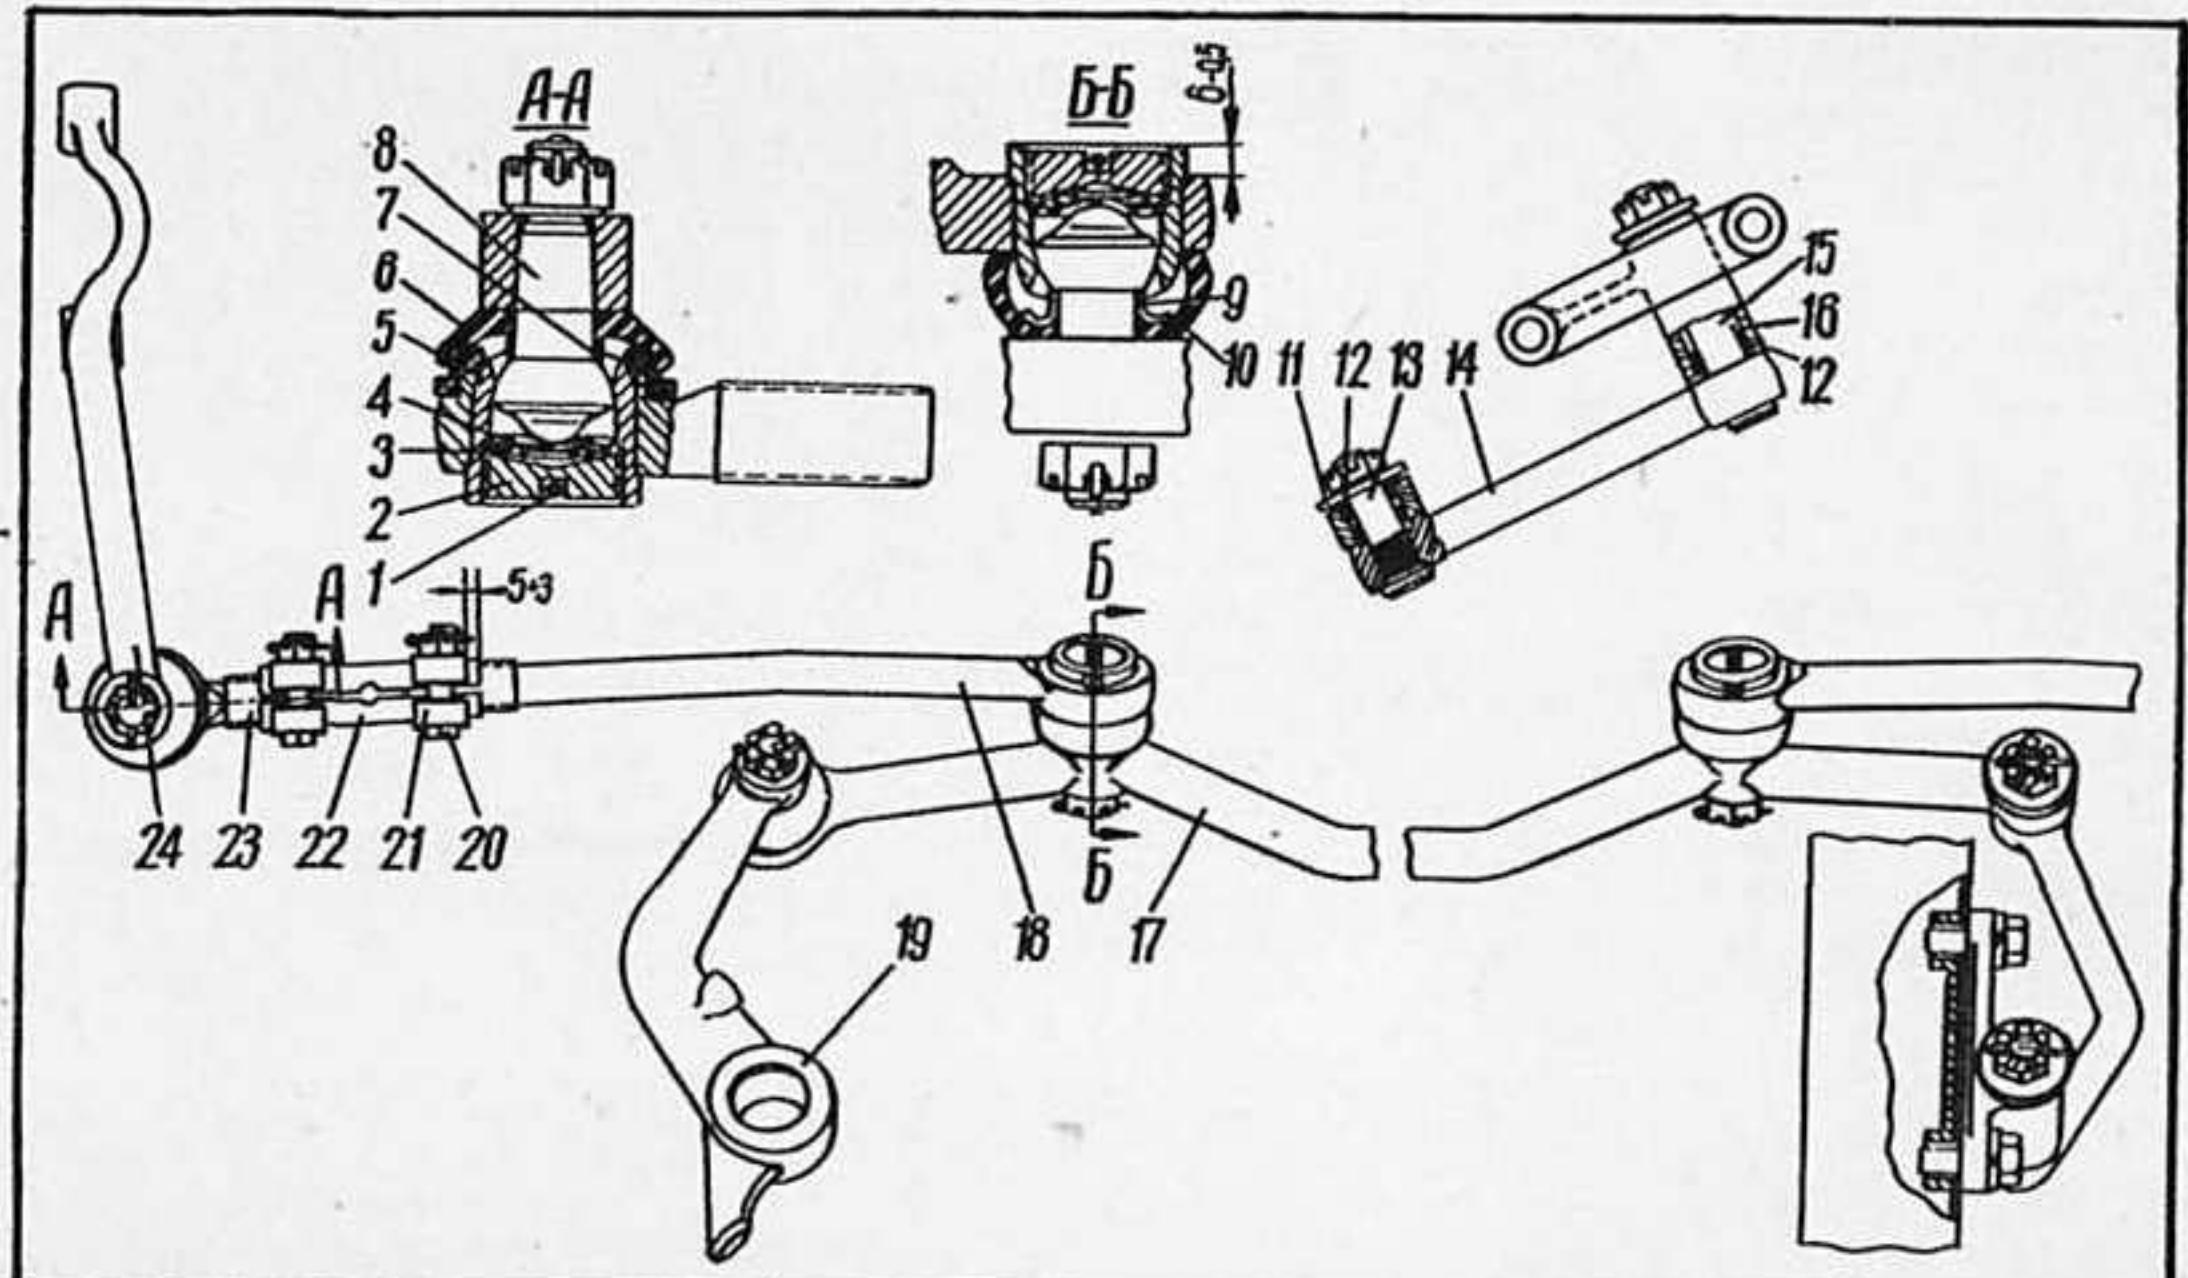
Рулевая трапеция: 1 — шплинт; 2 — заглушка шарнира; 3 — пружина; 4 — опорная пята; 5 — корпус шарнира наконечника тяги; 6 — уплотнитель шарнира; 7 — втулка шарового пальца; 8 — шаровой палец; 9 — втулка пальца боковой тяги; 10 — уплотнитель шарнира боковой тяги и тяги сошки; 11 — шайба; 12 — втулка маятникового рычага; 13 — передний палец маятникового рычага; 14 — маятниковый рычаг; 15 — задний палец маятникового рычага; 16 — кронштейн; 17 — тяга сошки; 18 — боковая тяга; 19 — сошка; 20 — болт; 21 — стяжной хомут; 22 — регулировочная трубка; 23 — наконечник тяги; 24 — поворотный рычаг.
